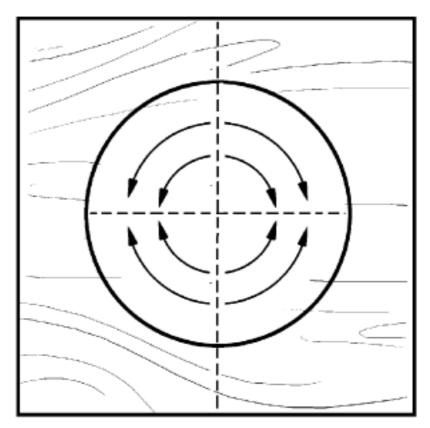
Выполнение круглой выпуклой формы на пласти заготовки (стрелками указано направление движения инструмента)
